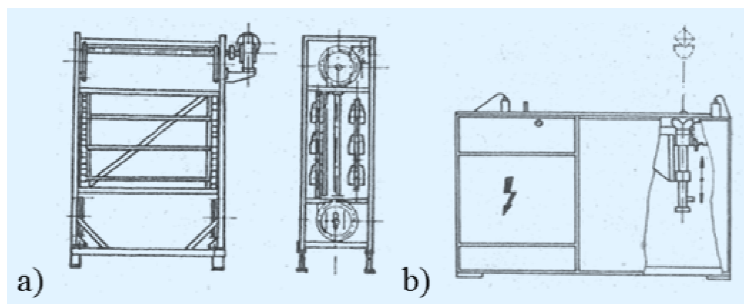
Příklad konstrukcí válečkových dopravníků
